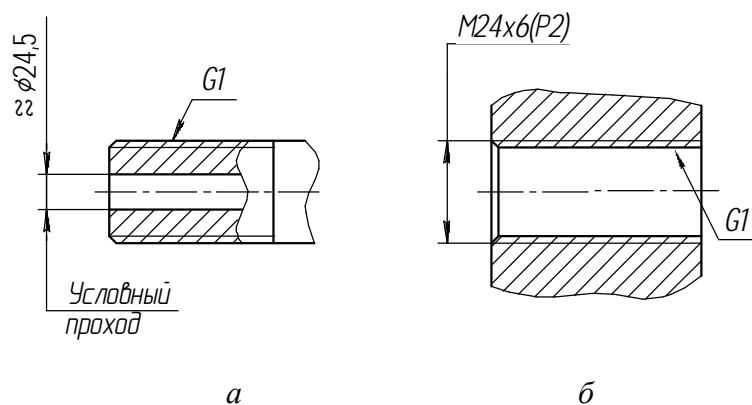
Нанесение размеров трубной цилиндрической резьбы:
